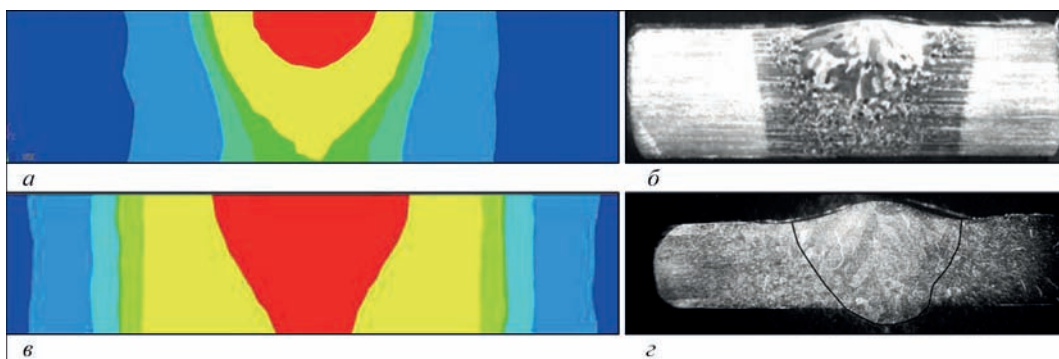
Проверка адекватности разработанной математической модели: а – на примере ТИГ сварки двухфазного высокопрочного титанового сплава ВТ23, б – на примере ТИГ сварки псевдо-β-титанового сплава ВТ19
